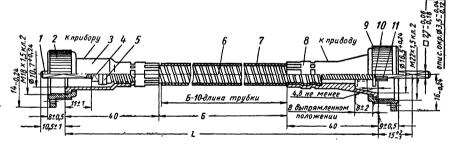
Комплектный разборно-запирающийся привод спидометра: 1 — гибкий вал; 2, 9 — накидные гайки; 4 — обжимная втулка; 5 — шайбы; 6 — броня; 7 — хлорвиниловая трубка; 10 — разрезная пружинная шайба; 11 — обжимная запорная муфта
